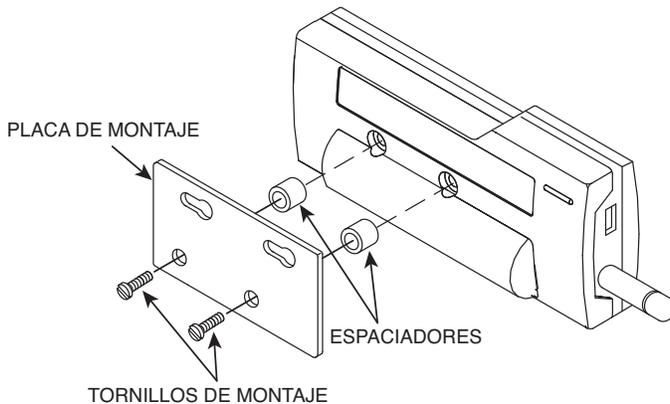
A. Instalación del soporte de montaje UWTC-1, UWTC-2, UWRTD-1, UWRTD-2
